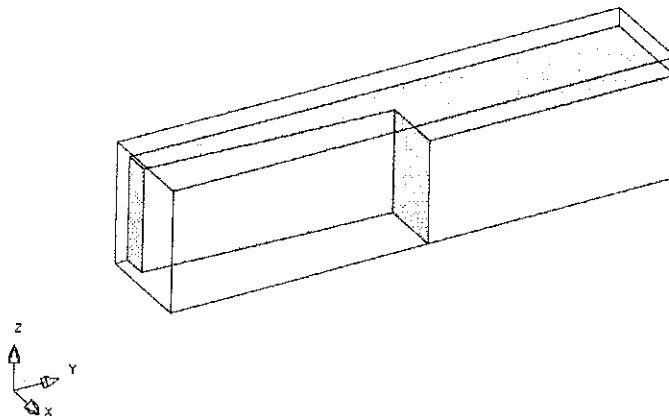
Echantillon de paquet de tôles qui simule une demie dent de partie frontale d'une machine
